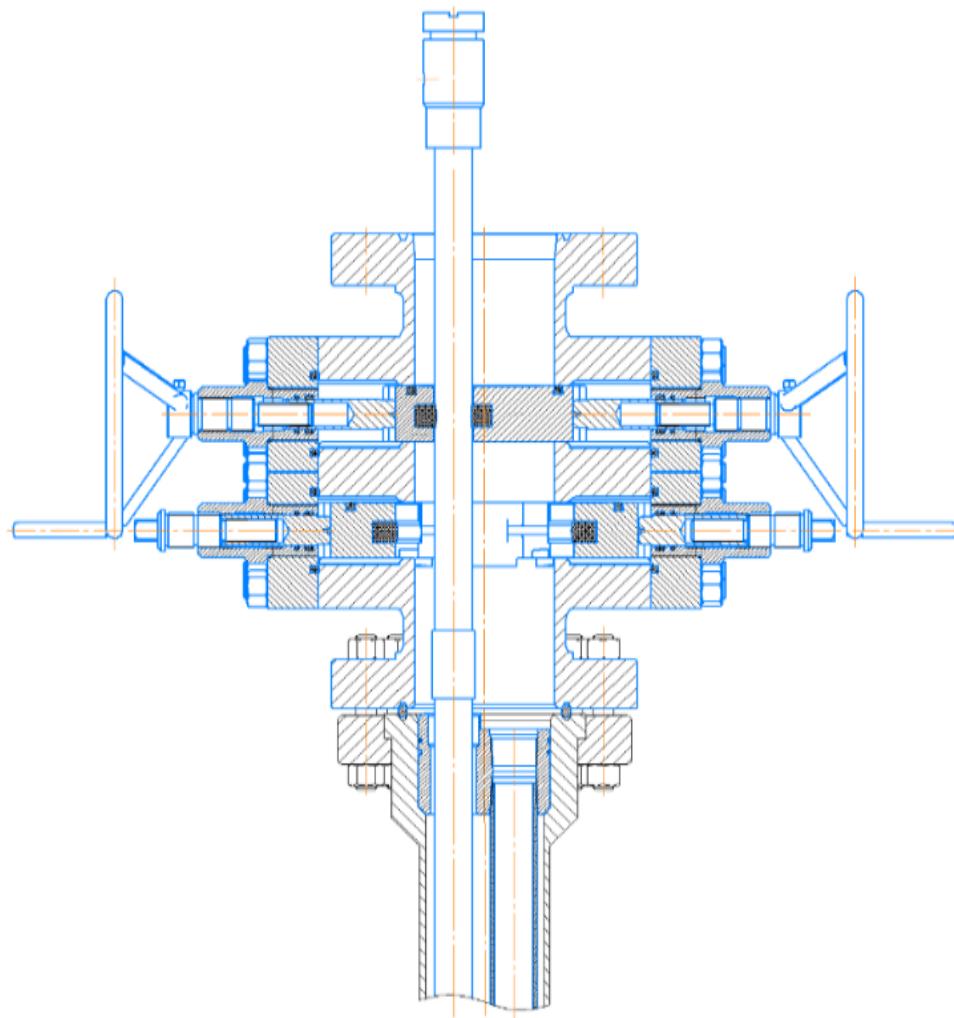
Усовершенствованный двухрядный превентор ППС-2Ф-180×21-2К
